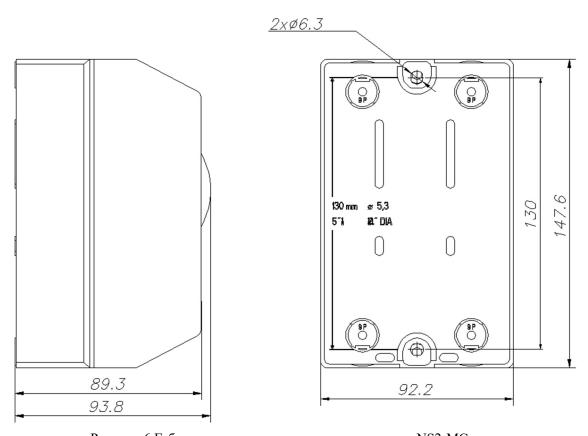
Габаритные и присоединительные размеры NS2-MC
